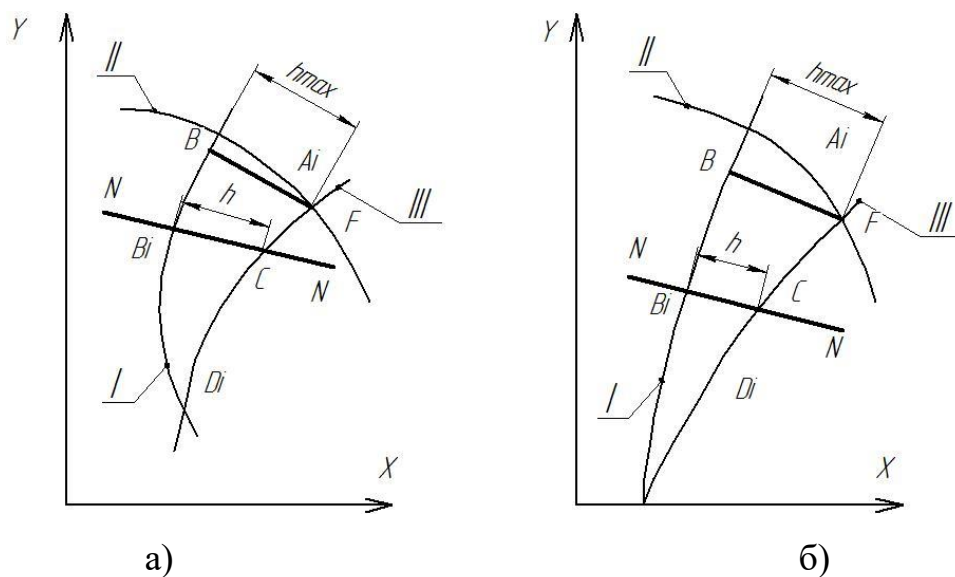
Розрахункові схеми для визначення товщини зрізуваного шару h для зустрічного (а)) та попутного (б)) фрезоточіння
